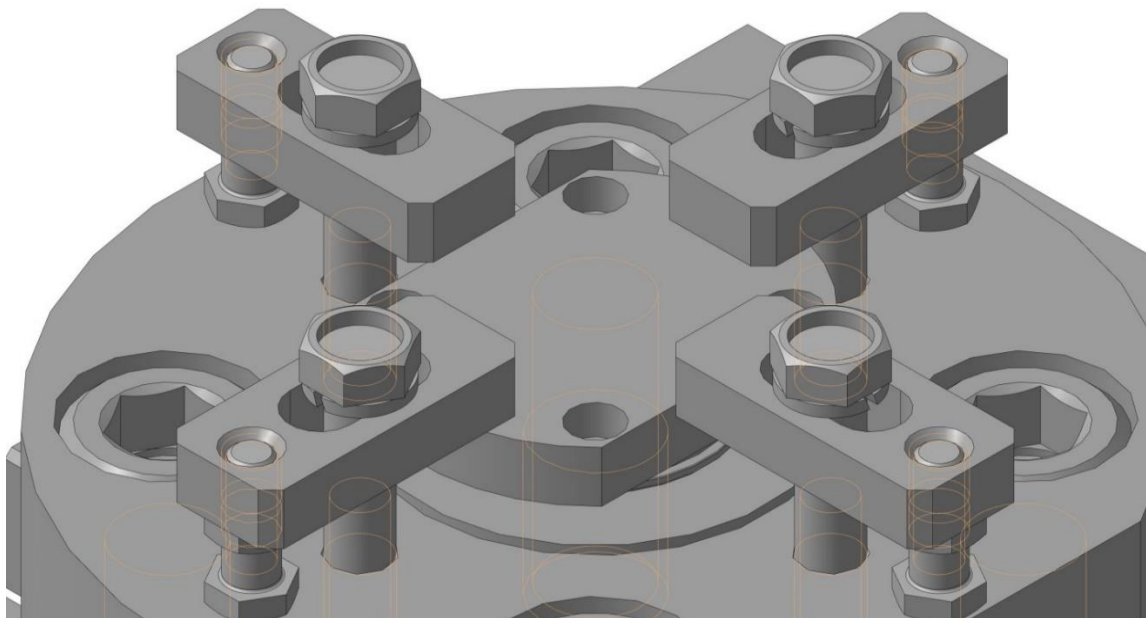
Приспособление с двумя дополнительными прижимами
